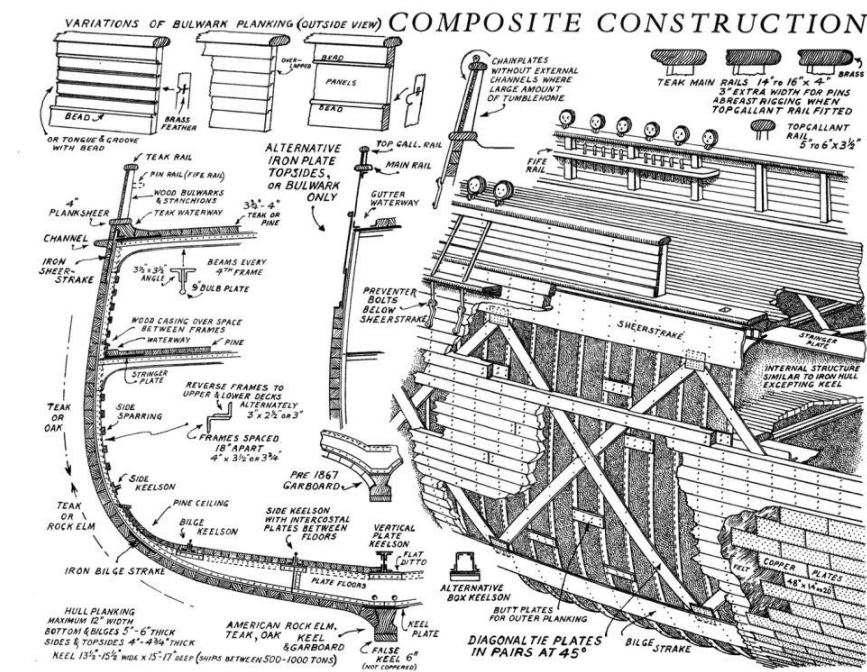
Detalles de la construcción compuesta. – Fuente: Google imágenes
